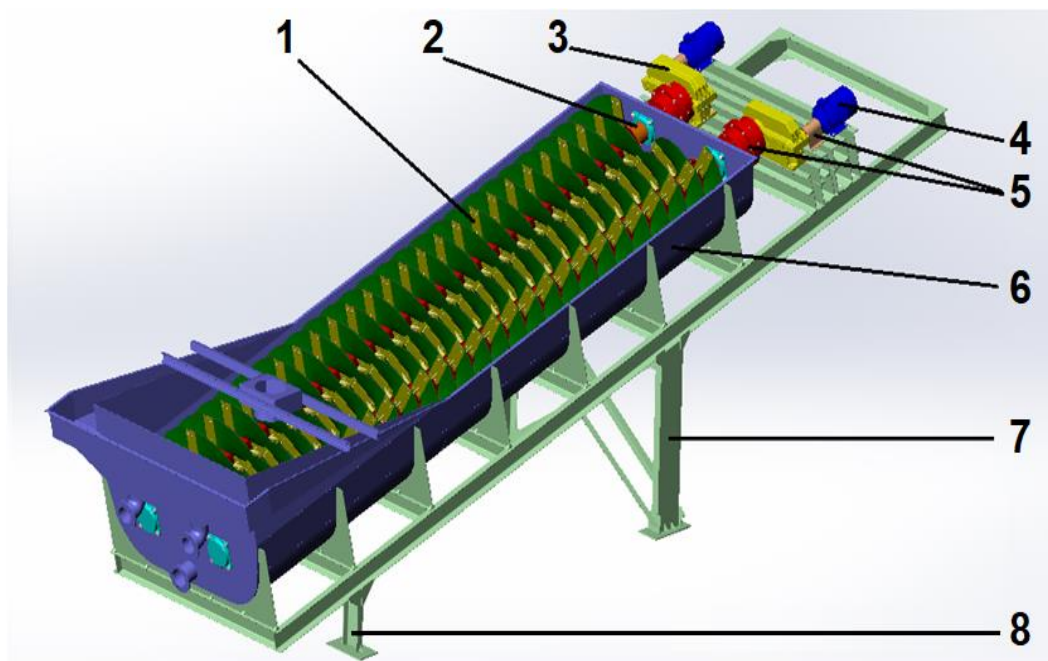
Будова спірального класифікатора: 1 – спіраль з лопатями; 2 – вал; 3 – редуктор; 4 – двигун; 5 – муфти; 6 – рама-корито; 7 – верхня опора; 8 – нижня опора.
